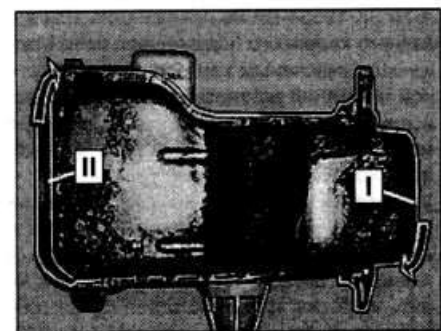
Порядок затяжки болтов крепления масляного картера
